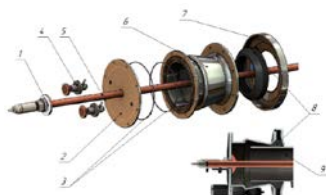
Конструктивные элементы фланца: 1 – токоввод; 2 – фланец-заглушка; 3 – уплотнительные кольца; 4 – натекатели; 5 – анод; 6 – прижимной фланец; 7 – ответный фланец; 8 – уплотнение; 9 – напыляемая труба
